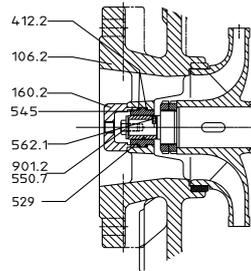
Desmontaje del cojinete liso: boca de aspiración axial
